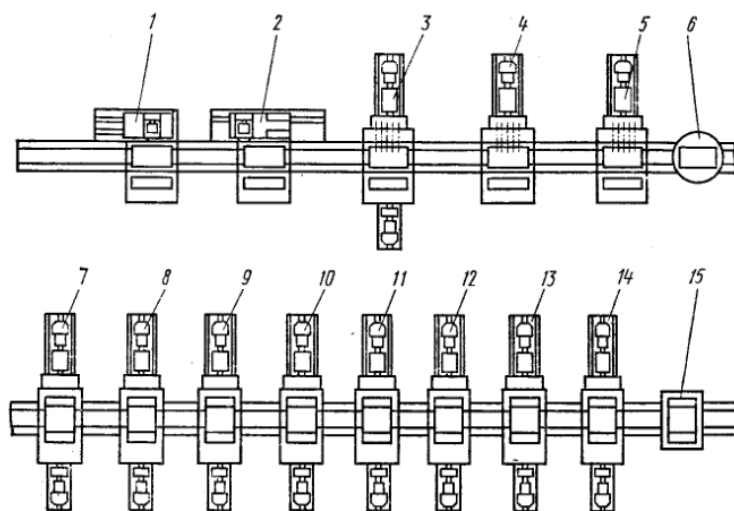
Планировка автоматической линии для обработки корпусных деталей:
